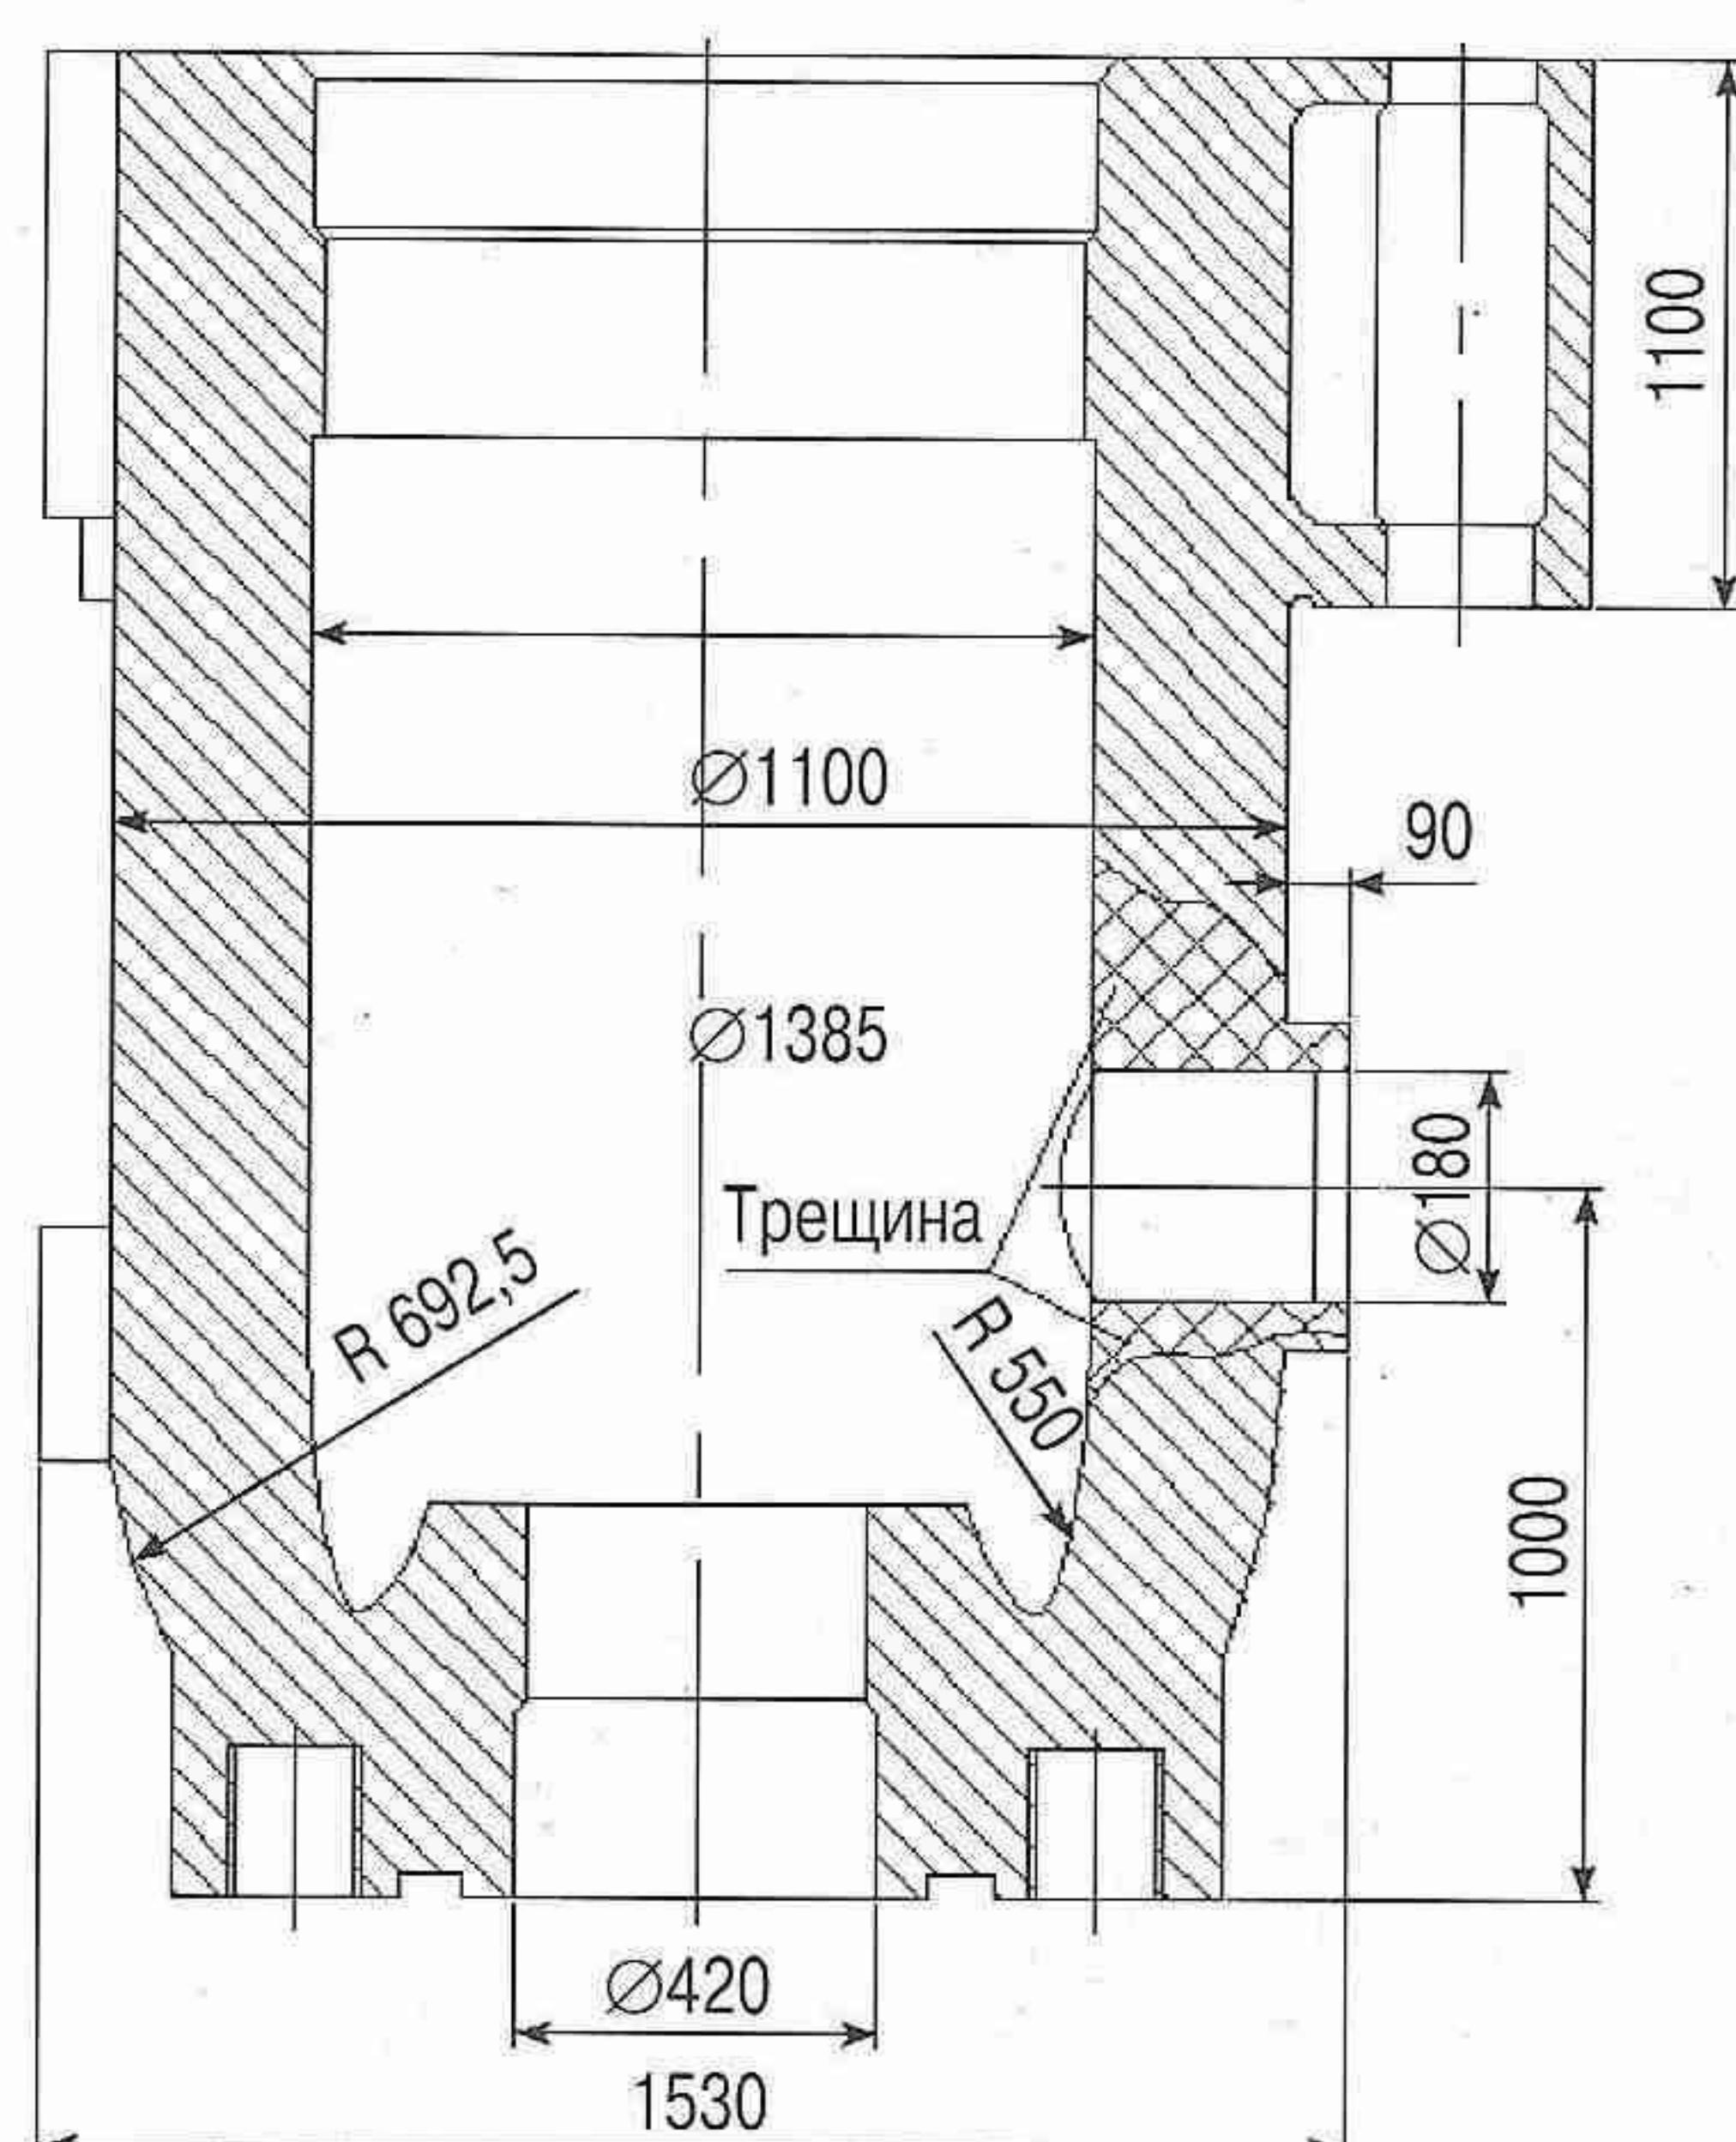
Цилиндр пресса силой 18 МН, разрушенный по отверстию для подвода рабочей жидкости
